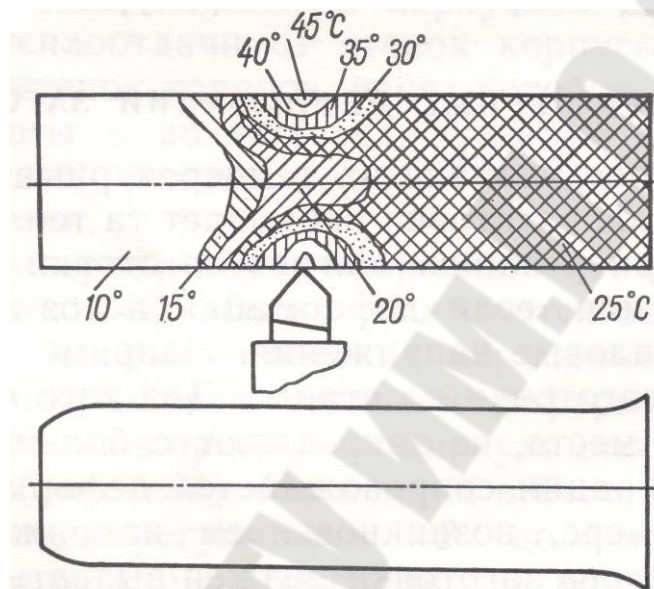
Температурное поле обрабатываемой заготовки и ее форма после обработки
